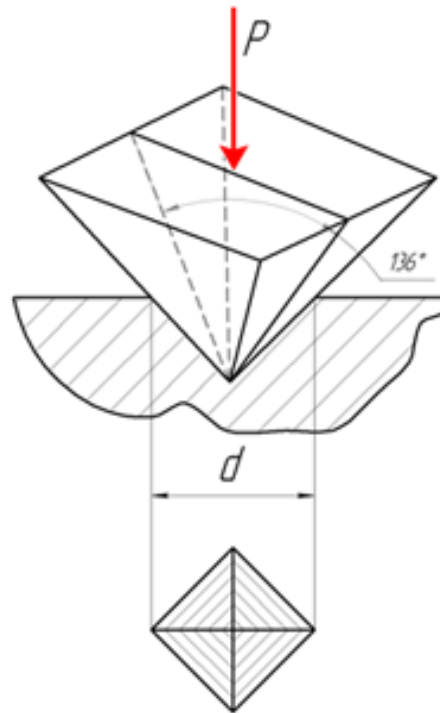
Схема вимірювання твердості за Віккерсом
